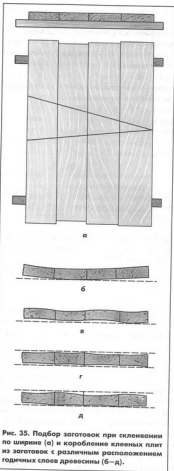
Подбор заготовок при склеивании по ширине (а) и коробление клееных плит из заготовок с различным расположением годичных слоев древесины (б—д).
